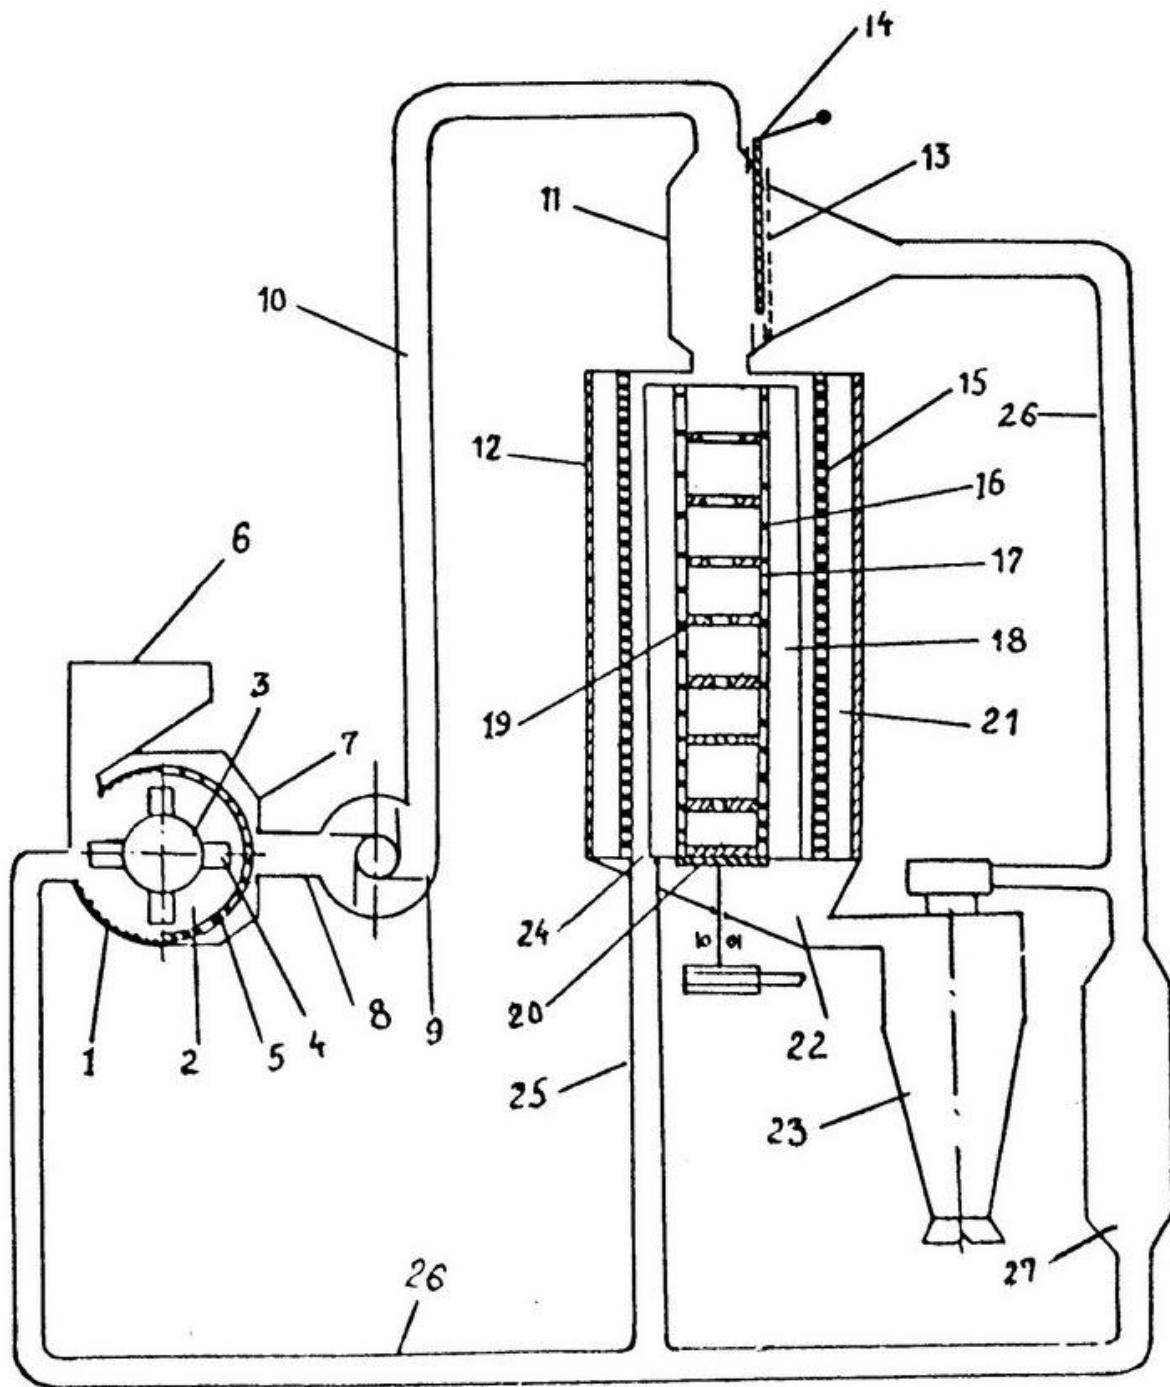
Общий вид дробилки кормов по патенту РФ № 2027343
